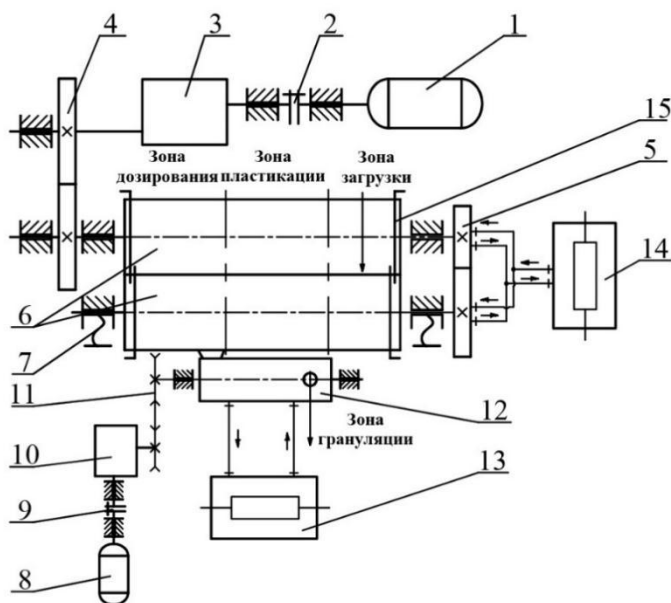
Схема лабораторної установки: 1 – електродвигун; 2, 9 – муфта; 3 – редуктор; 4 – передавальні шестерні; 5 – фрикційна передача; 6 – валки; 7 – механізм регулювання зазору; 8 – електродвигун відбіркового пристрою; 10 – черв'ячний редуктор; 11 – ремінна передача; 12 – відбірково-шнековий пристрій; 13, 14 – термостати; 15 – обмежувальні стріли
